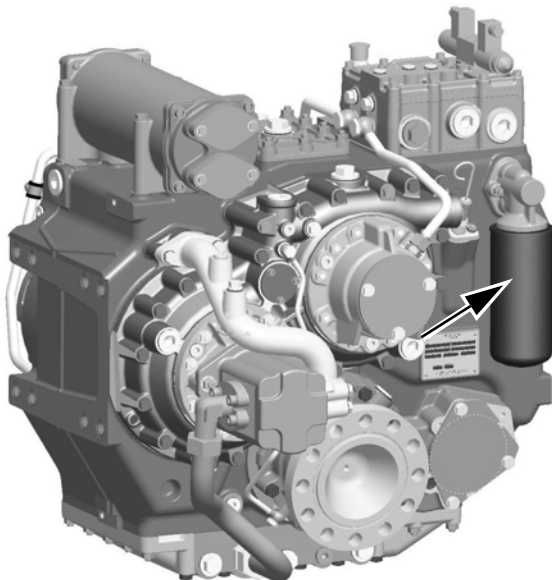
Ölfilter am Getriebe ZF 3150 A (Beispiel)
